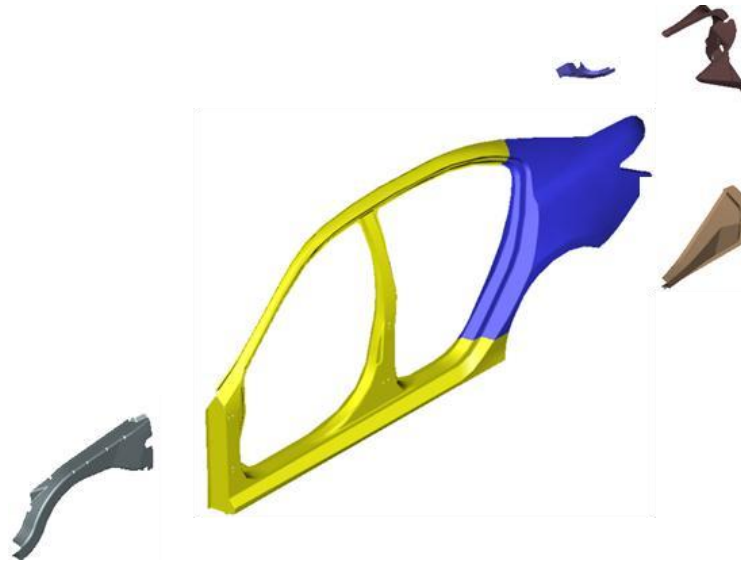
Зовнішня підбірка бічної частини кузова з точковою зваркою.
